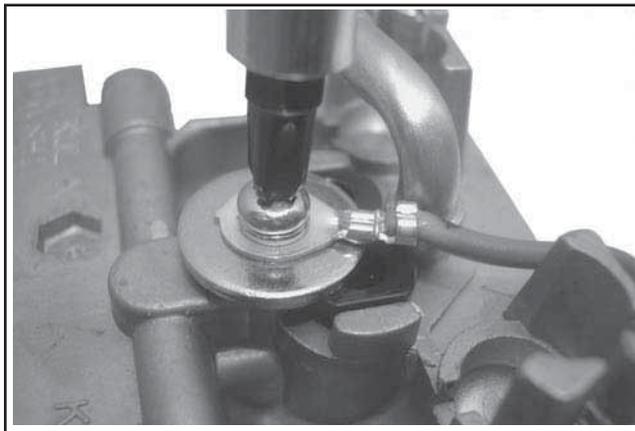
Connexion du câble de terre (carburateur bicylindre).
